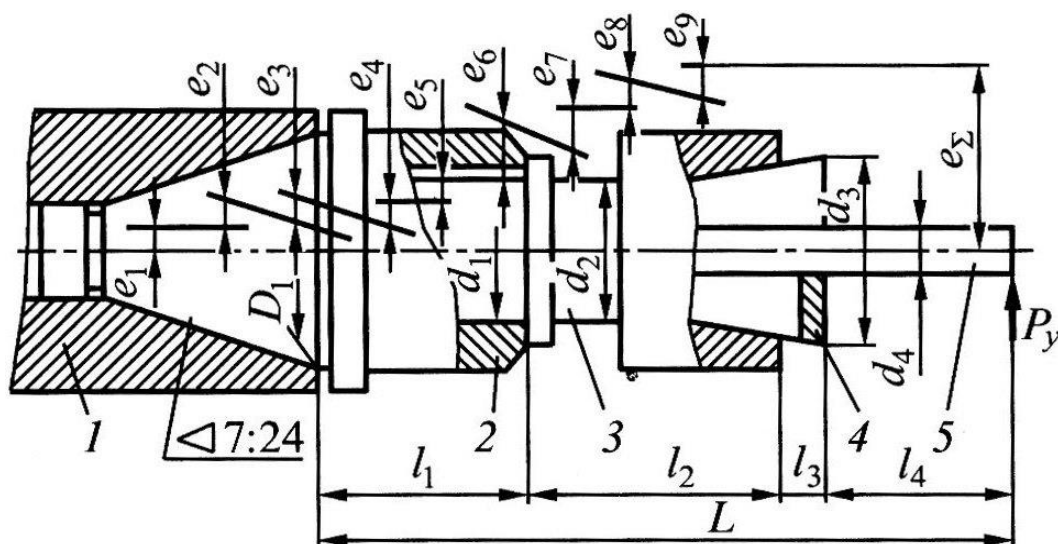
Размерная цепь сборки АСП и режущего инструмента по рис. 2, установленной на станке: 1 – шпиндель станка; 2 – базисный агрегат; 3 – сменная наладка; 4 - цанга
